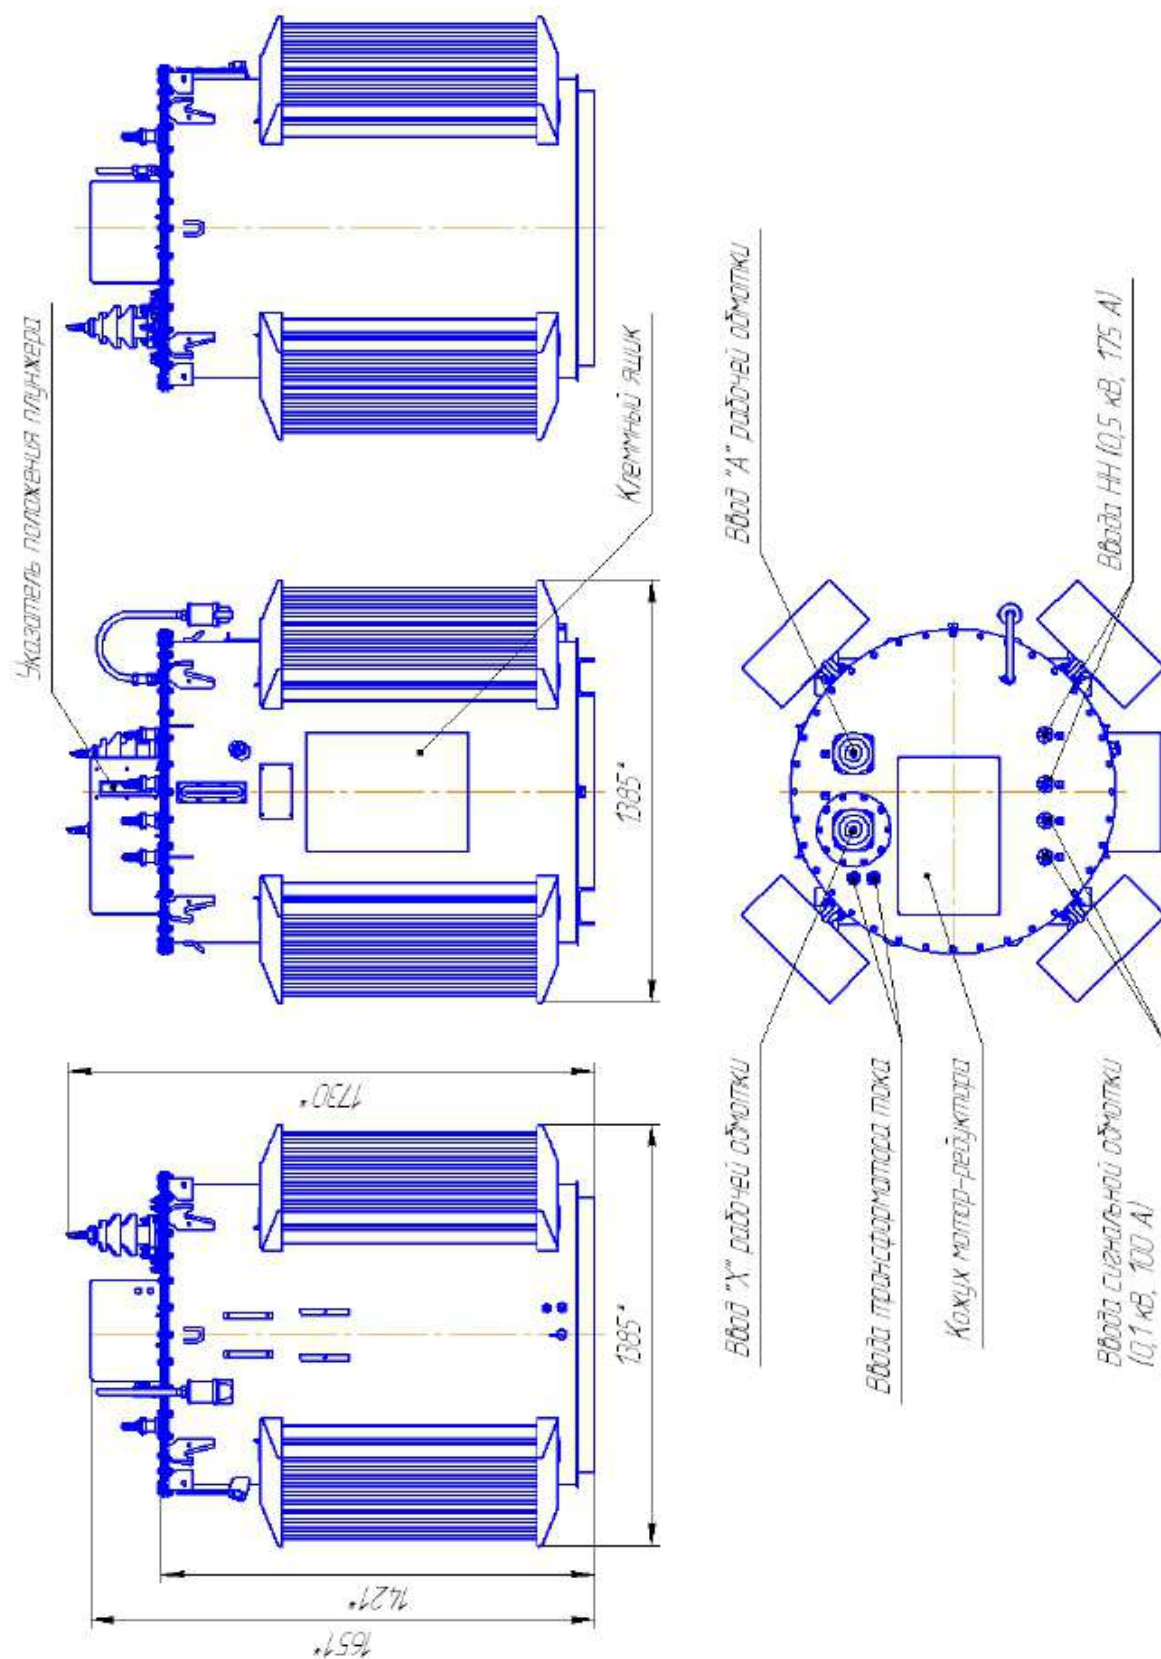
Общий вид дутогасящего реактора РДМРА
